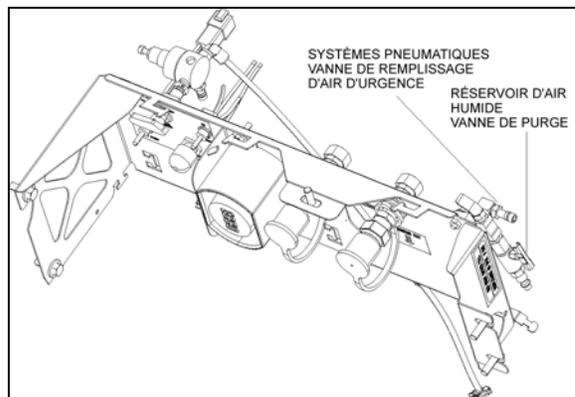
EMBLACEMENT DE SOUPAPE ARRIÈRE SUR LA SÉRIE H3
